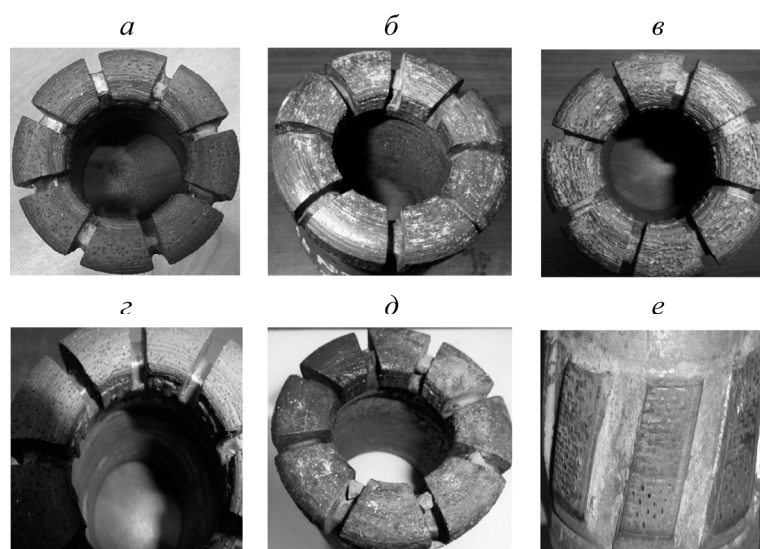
Фотографии отработанного алмазного инструмента нестандартного наружного диаметра: *a* — 17ИЗГ-12-78-1; *б* — 17ИЗГ-12-78-2; *в* — 17ИЗГ-12-78-3(пилот); *г* — 17ИЗГ-12-78-3 (внутренний диаметр); *д* — 17ИЗГ-12-78-4; *е* — РЦК-78.4-1
